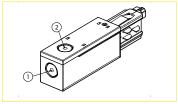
Pareti sfondabili della testata Pic. 2 Knock-out walls
